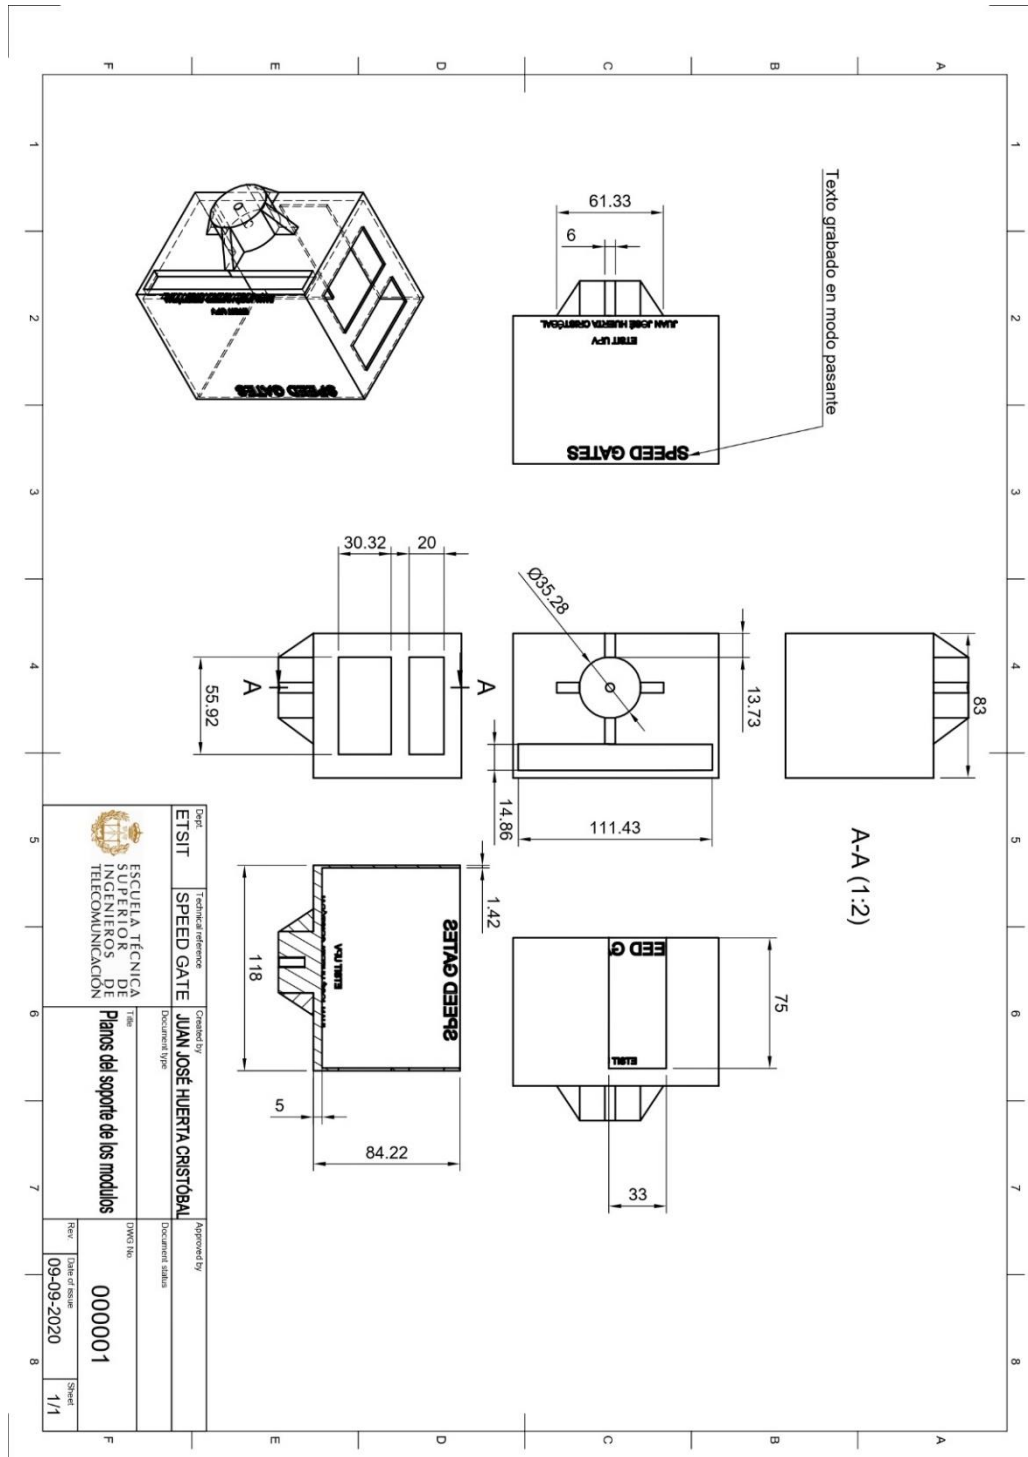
Plano de alzado, planta y vistas laterales del Soporte.
